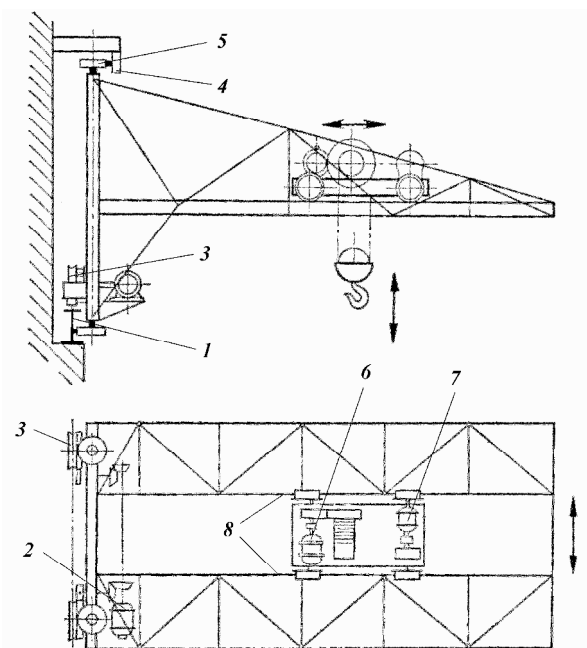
Macara în consolă cu braț fix: 1- șină rulare macara; 2- motor acționare meca-nism rulare macara; 3- roți de rulare; 4- ghidaj; 5- rolă sprijin; 6- motor acționare palan; 7- motor pentru deplasare căru-cior; 8- căi de rulare cărucior.
